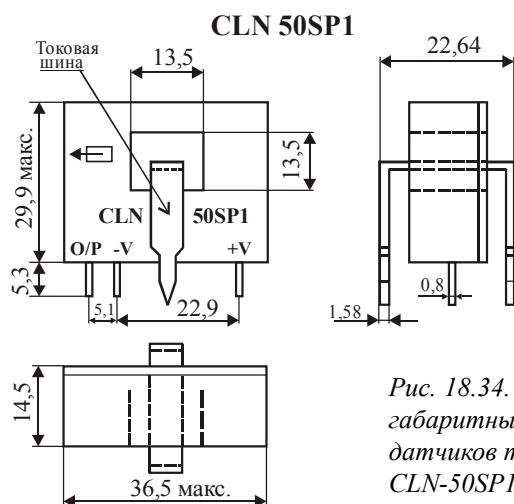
Внешний вид и габаритные размеры датчиков тока типа CLN-50SP1, CLN-100SP1
